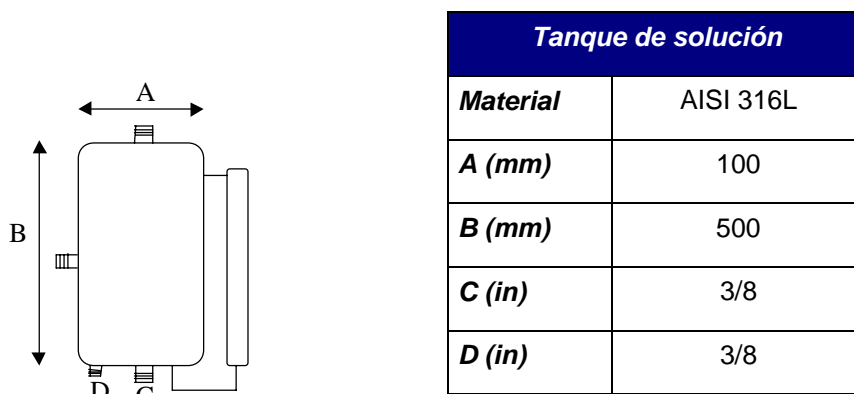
Dimensiones del tanque usado como tanque de solución.
